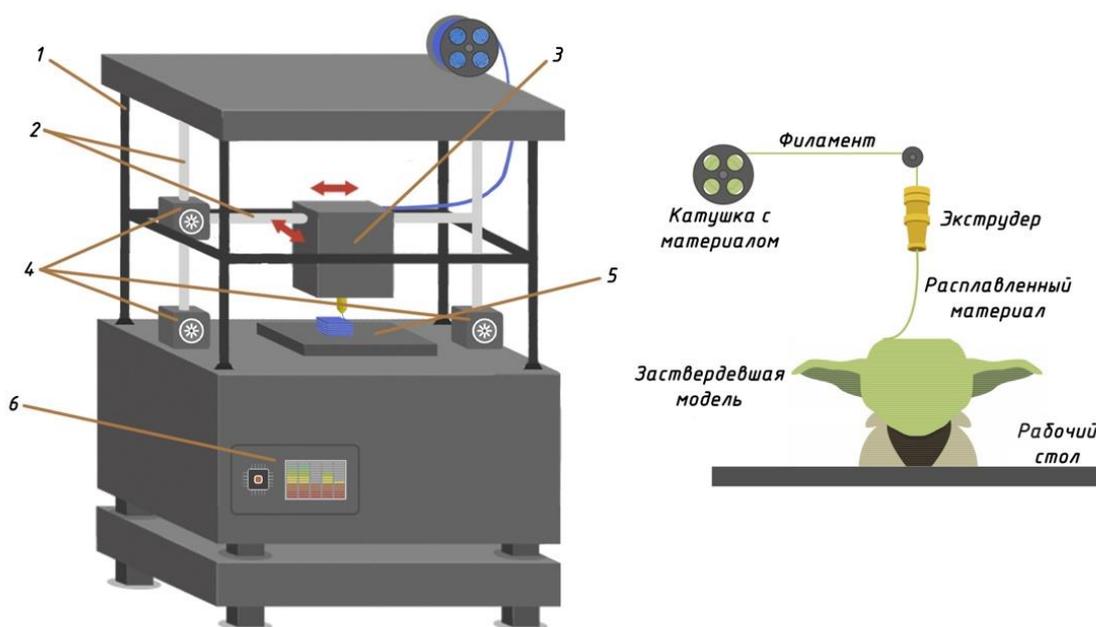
Схема устройства 3D-принтера экструзивного типа:
